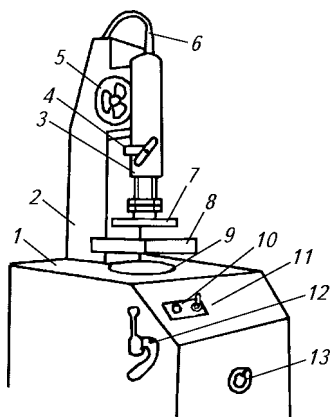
Общий вид лабораторной вакуум-формовочной машины:
